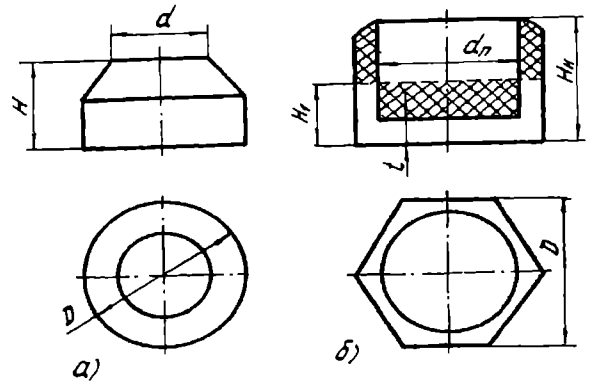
Цилиндроконическая заготовка (а) и схема к определению ее размеров (б)
